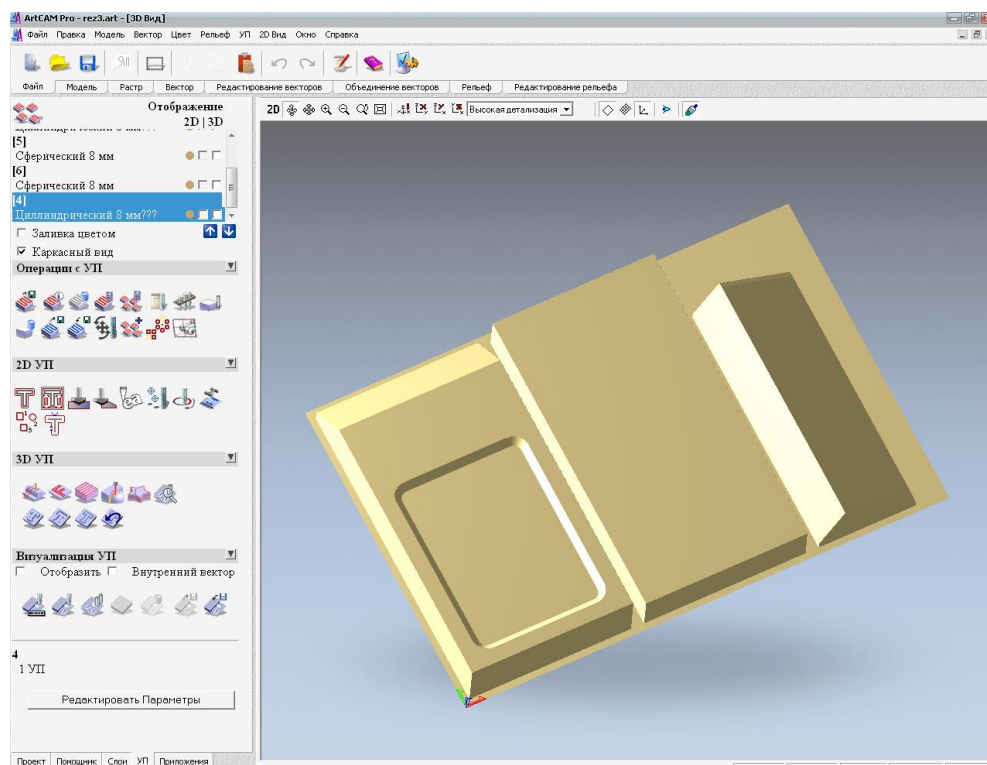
Деталі, що отримуються з третьої заготовки, розташовані на робочій площині
